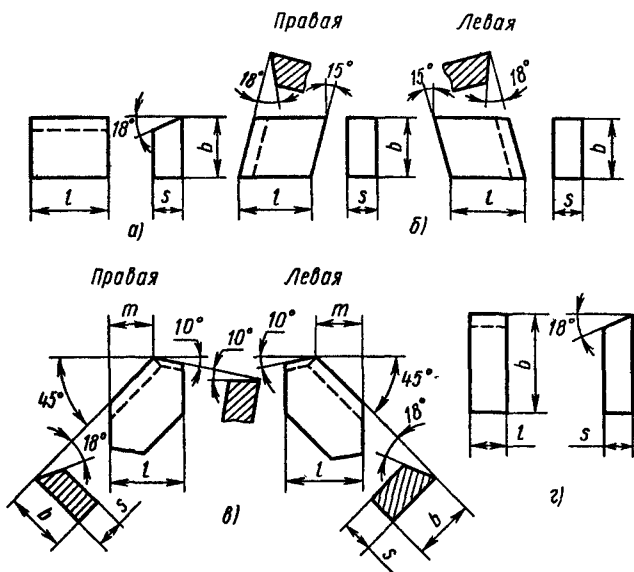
Формы напайных пластин из быстрорежущей стали для резов
